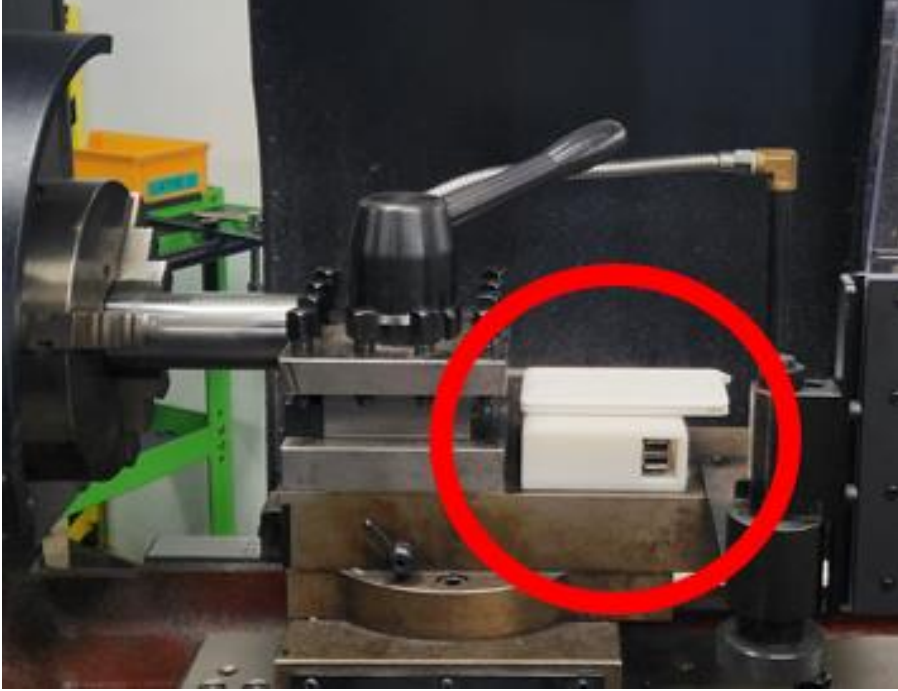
Tool Slide에 부착한 데이터 수집 실험 사진
